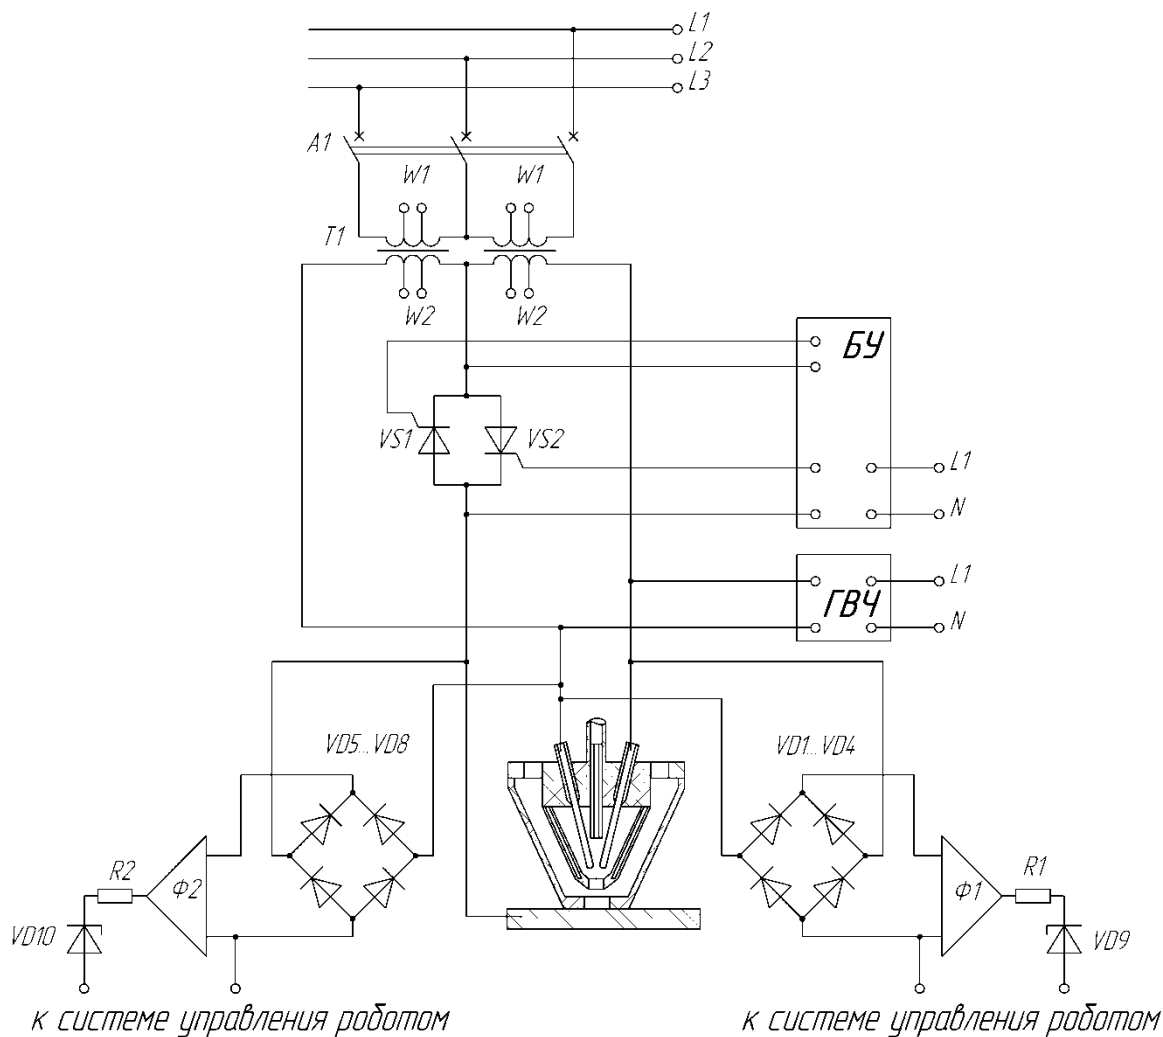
Принципиальная схема сварочной установки
